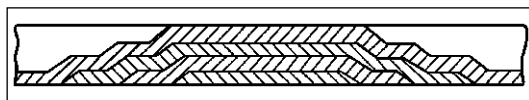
Схема сварки конусообразной вставки в отверстие диаметром более 50 мм
